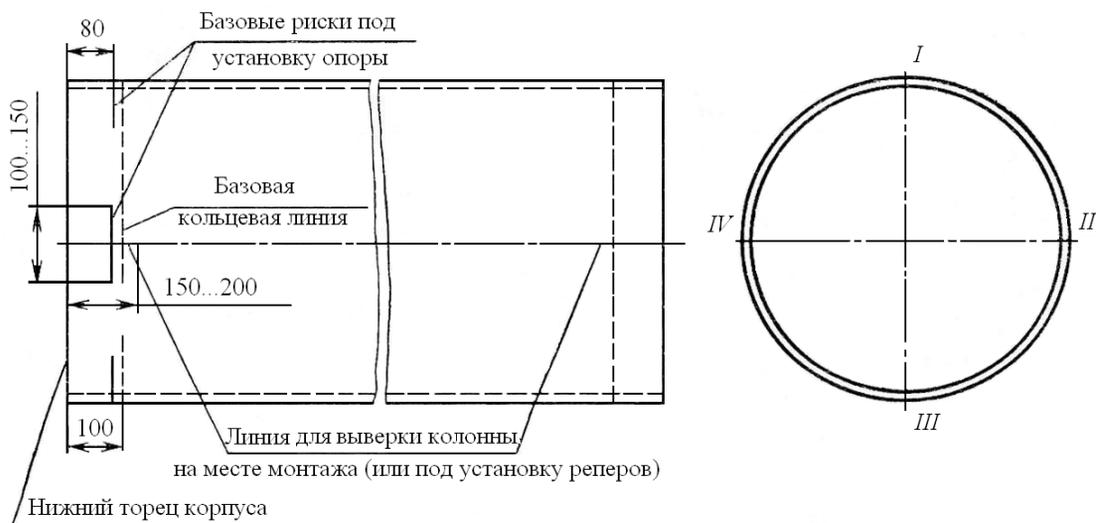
Схема нанесения рисок для установки опоры и выверки колонны на монтажной площадке
